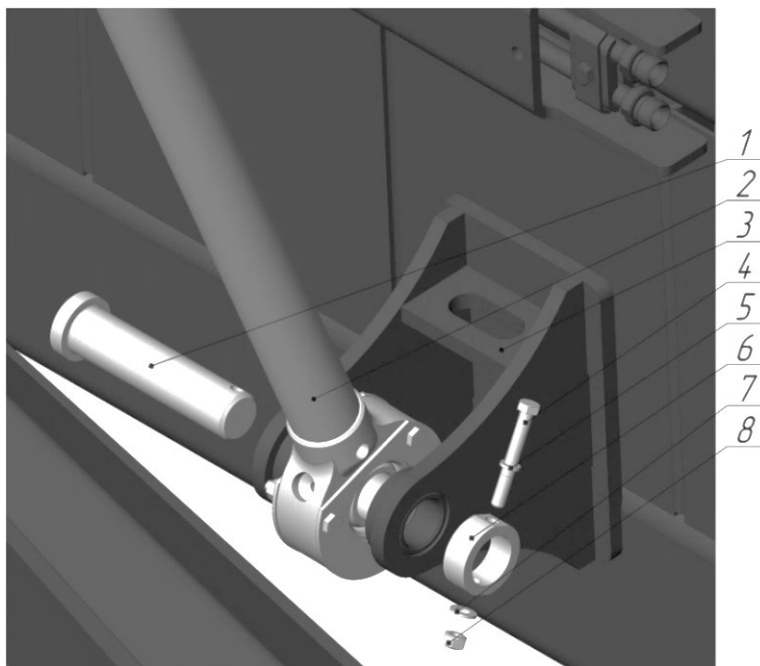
Гидроцилиндр подъема (опускания) отвала
